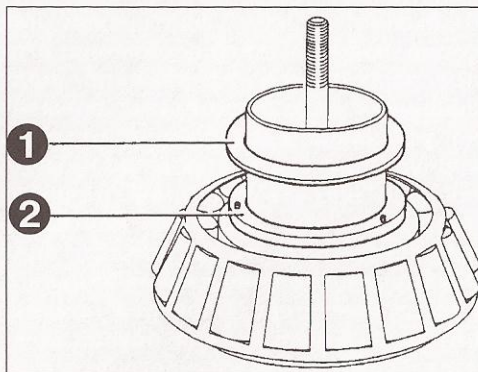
Установка специального приспособления для проверки предварительного напряжения подшипников дифференциала.
